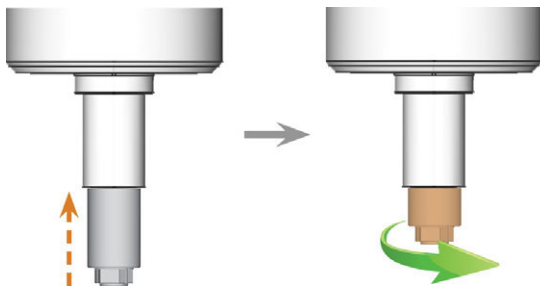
Spannzange (orange markiert in der rechten Abbildung) von Hand in die Spindel schrauben
